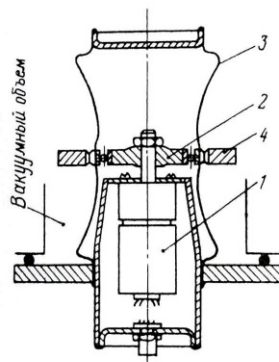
Схема герметичной волновой зубчатой передачи с внутренним генератором
